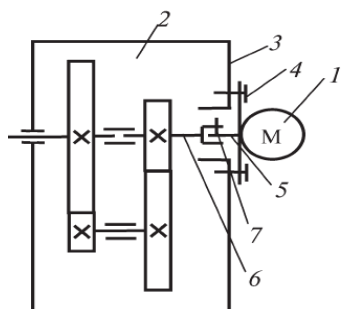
Соосный двухступенчатый редуктор Рис. 1.6. Червячный мотор-редуктор
